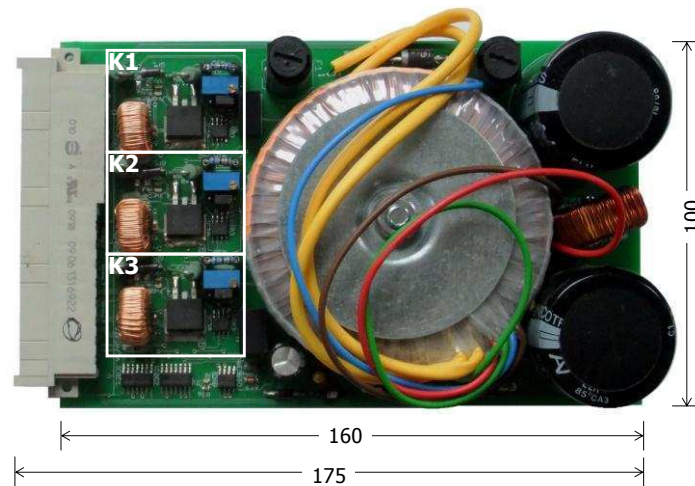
Bild einer HL-LED-Steuerung mit einem Ringkerntransformator zwei großen Kondensatoren (rechts im Bild). Die weißen Rechtecke grenzen die einzelnen Steuerkanäle (K1 bis K3) der jeweiligen HL-LEDs ein.
